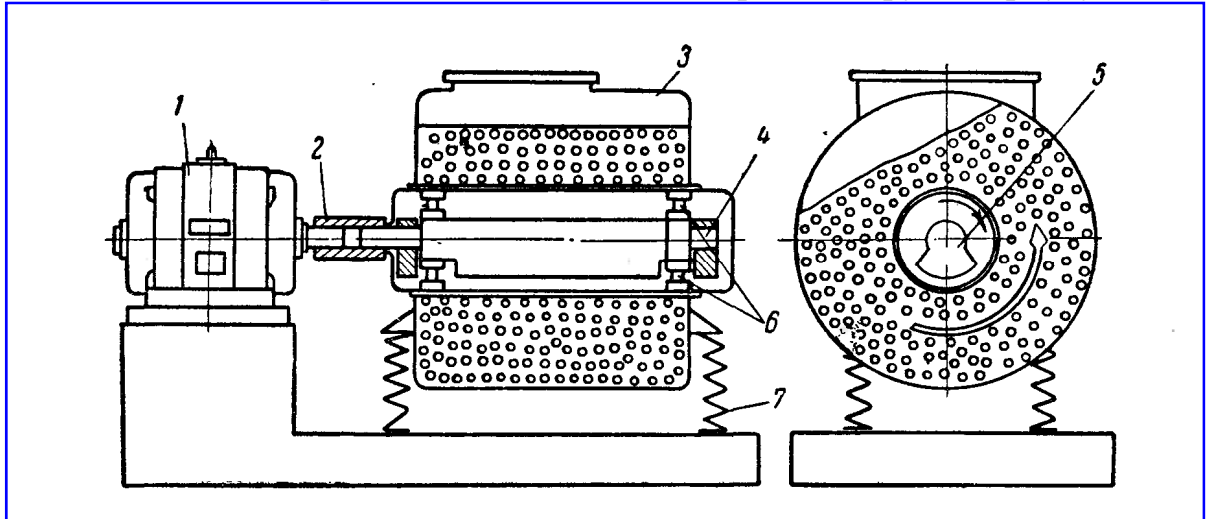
Схема вібраційного млина: 1 – електродвигун; 2 – еластична муфта; 3 – корпус; 4 – вал вібратора; 5 – дебаланс; 6 – підшипники; 7 – пружини.
